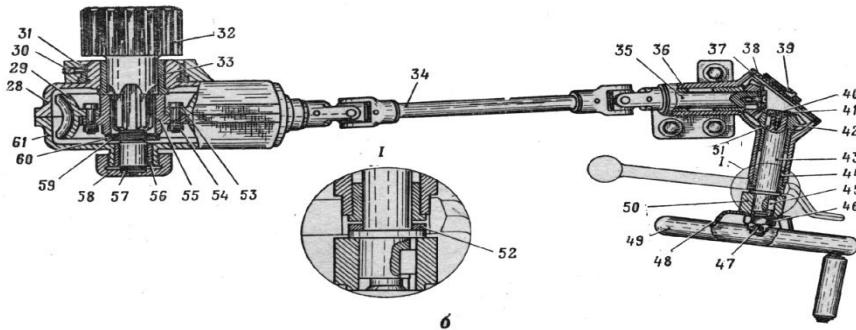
Підйомний механізм, вигляд зверху:
